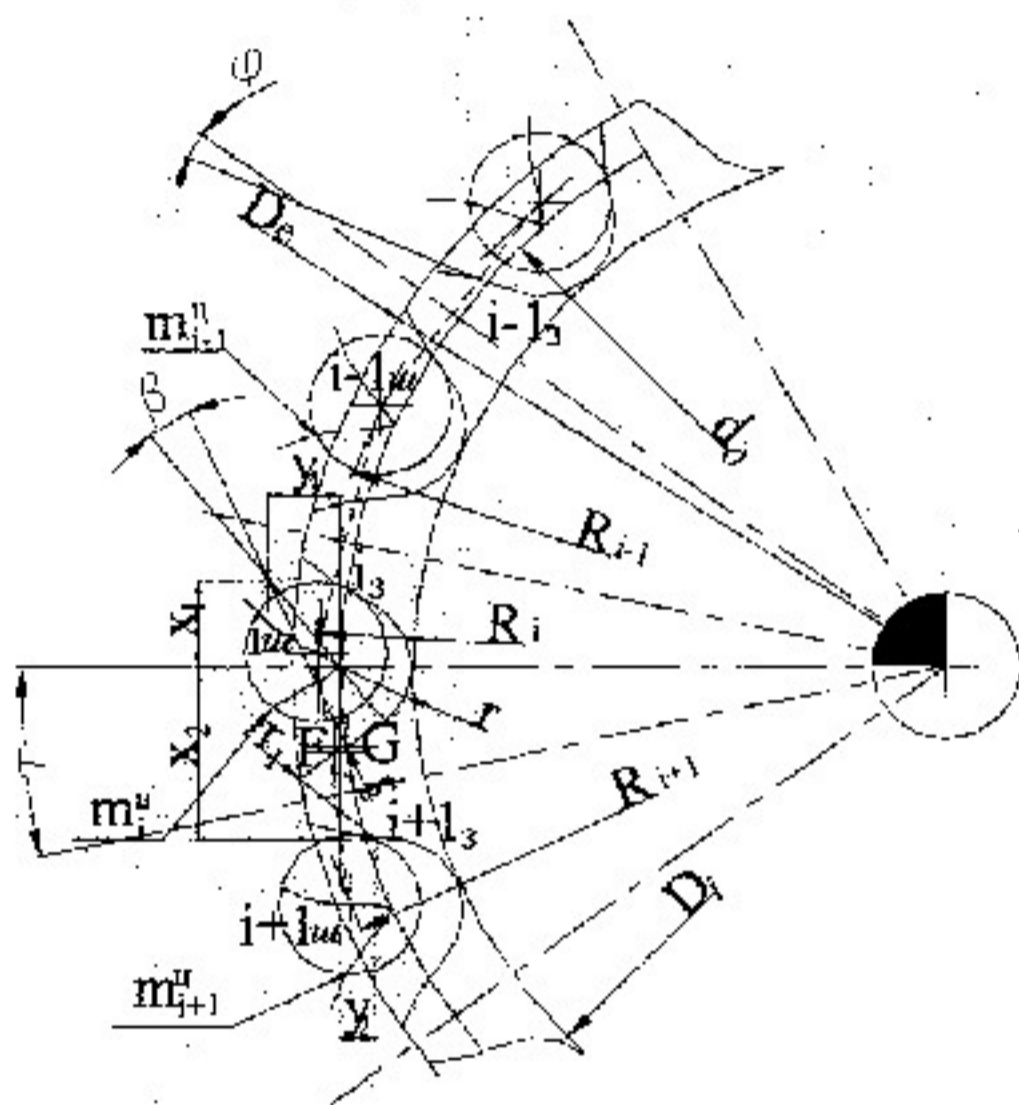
Элементы геометрии профиля звездочки и положения шарниров цепи
